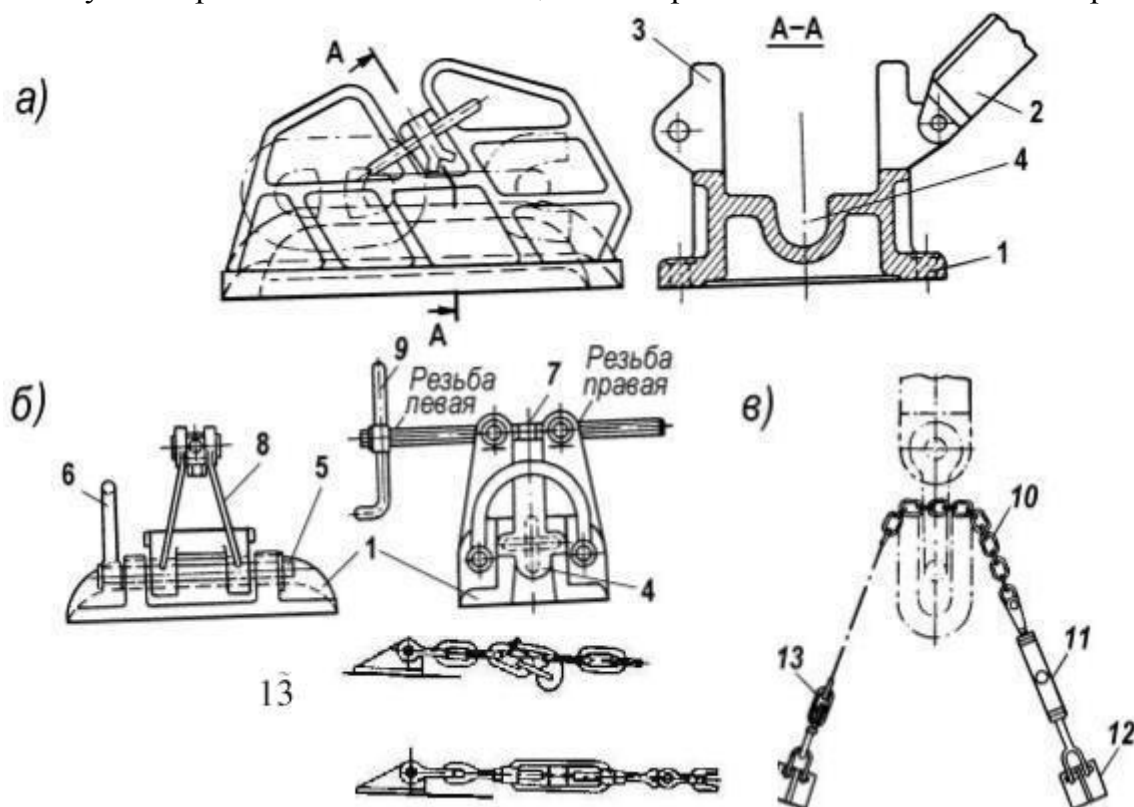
Конструкция стопоров якорной цепи: а–закладной, б–винтовой, в - цепной. 1 – плита - основание; 2- закладной пал; 3 – щека; 4 – желоб; 5 – штырь; 6 – дуга; 7 – винт; 8 – нащечина; 9 - рукоятка; 10 - цепочка; 11 - талреп; 12 - обух; 13 - глаголь-гак.
